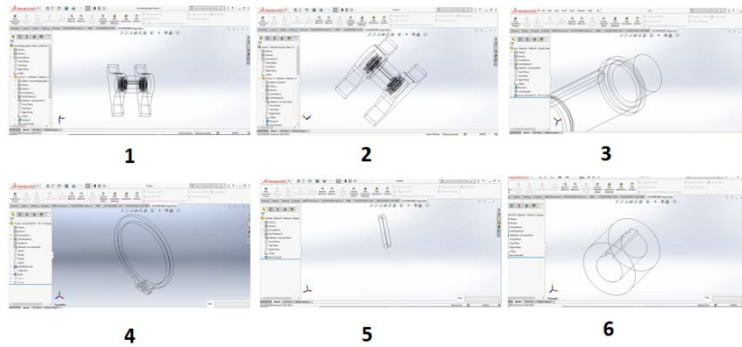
1 Assemblage palier milieu, 2 Galet, 3 Axe, 4 Circlips, 5 Clavette, 6 Galet milieu
